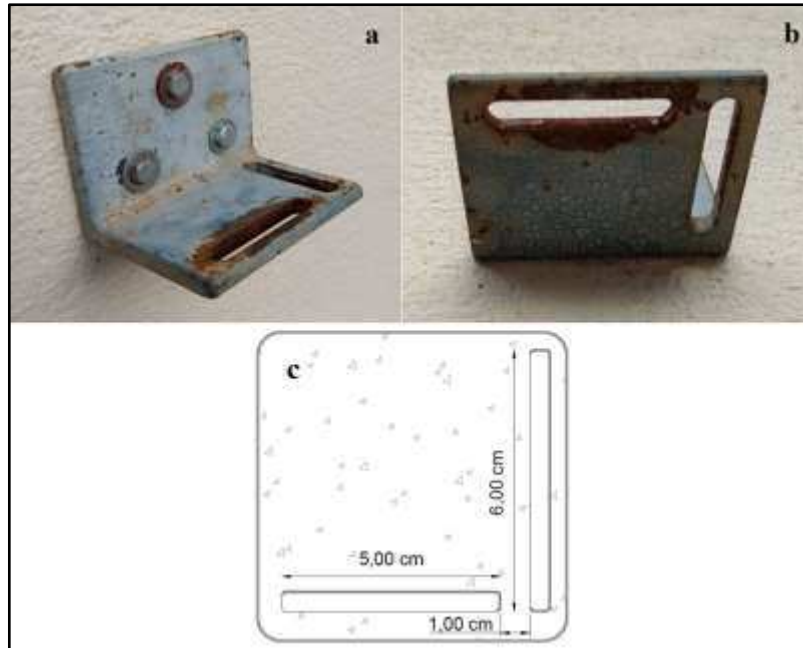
Placa metálica utilizada para suporte dos prismas no levantamento de campo. a: Vista superior da placa metálica; b: Vista inferior da placa metálica; c: Esquema com as dimensões da placa.
